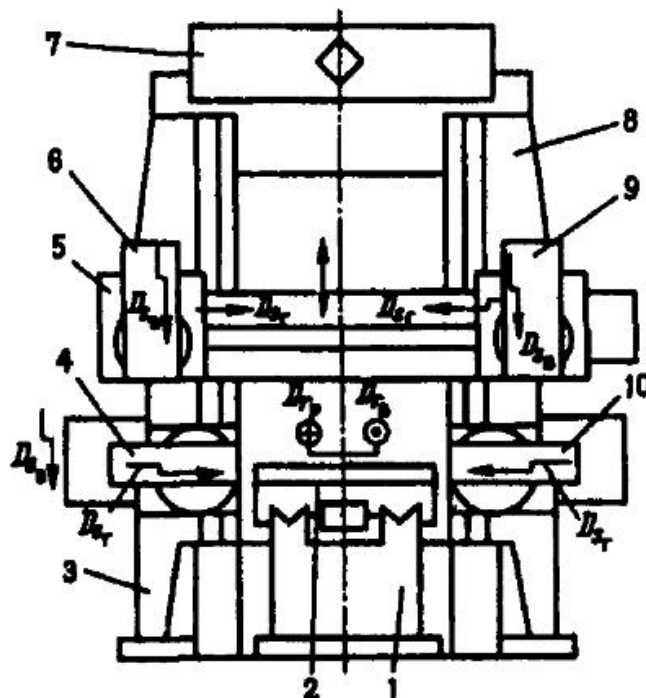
Загальний вигляд двохстійкового повздовжньо – строгального верстату
